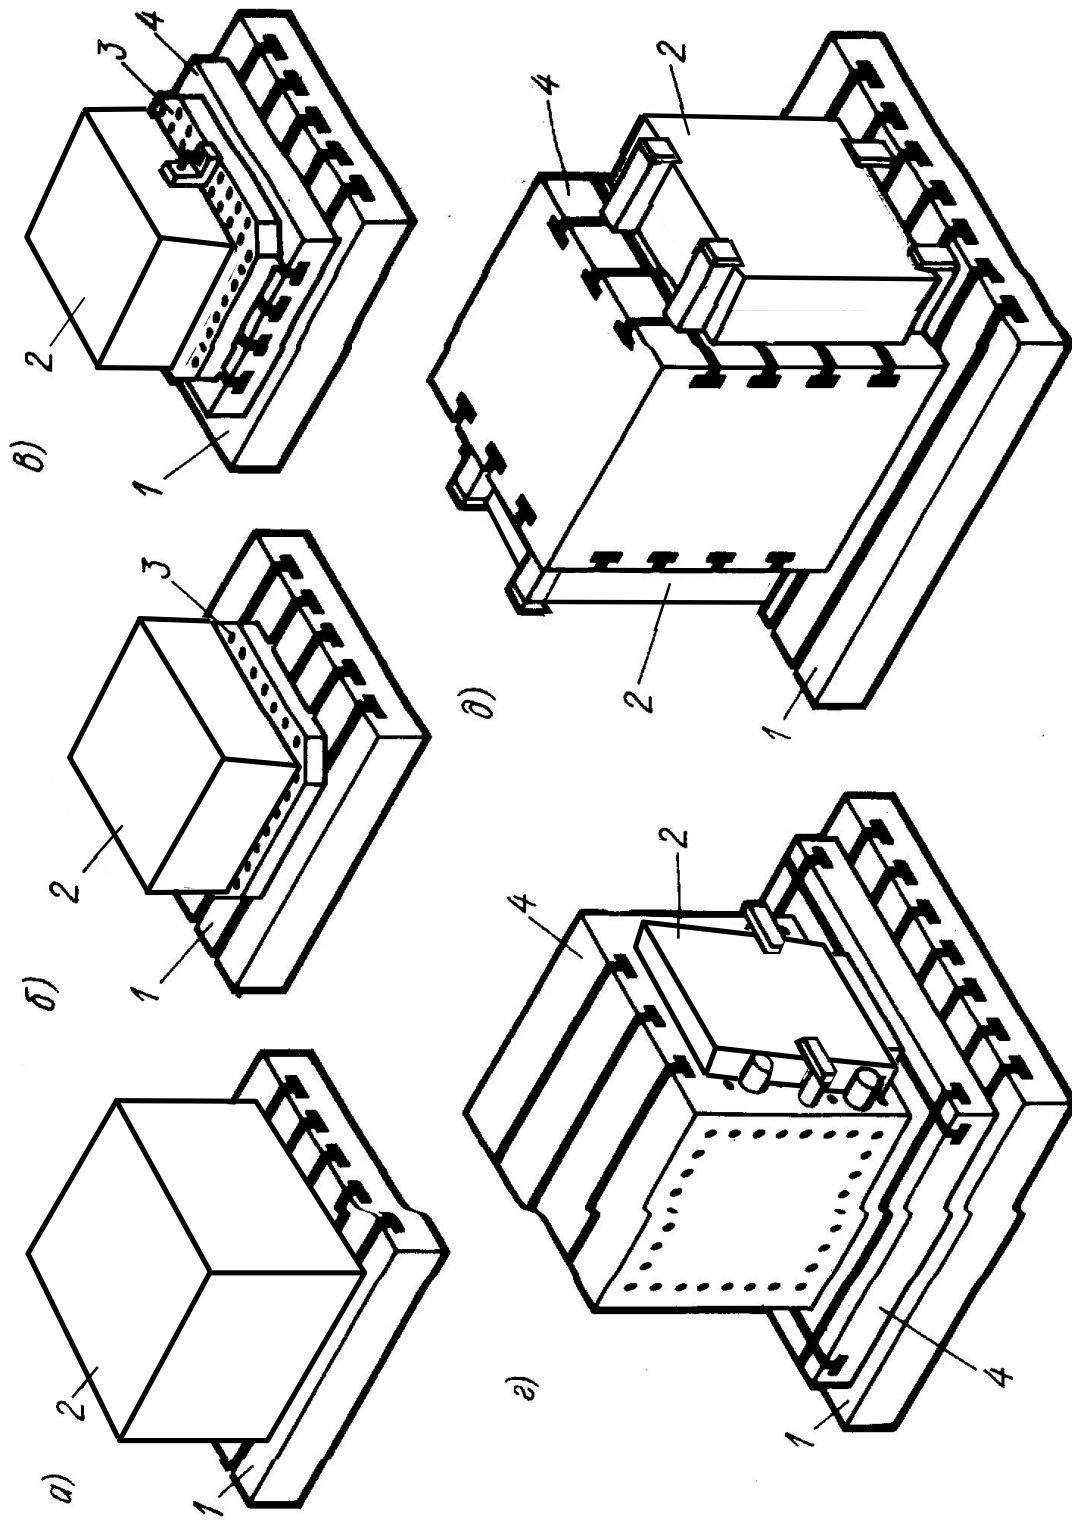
Схеми базування заготовок на столах верстагів з ЧПК: 1 – стіл верстага; 2 – заготовка; 3 – пристосування; 4 – координатна плита
